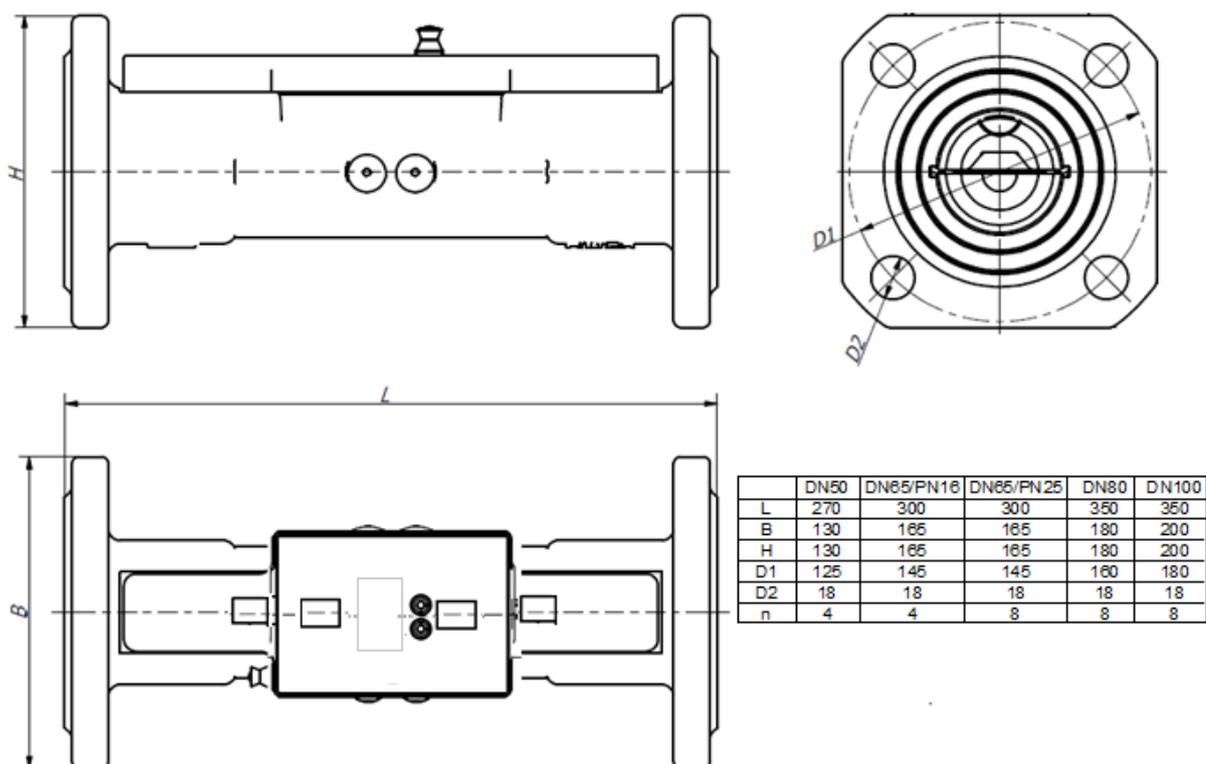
Габаритные размеры ультразвукового преобразователя расхода с Ду50, Ду50.1, Ду65, Ду65.1, Ду80, Ду80.1, Ду100.1, Ду100.2 (Латунный корпус)
